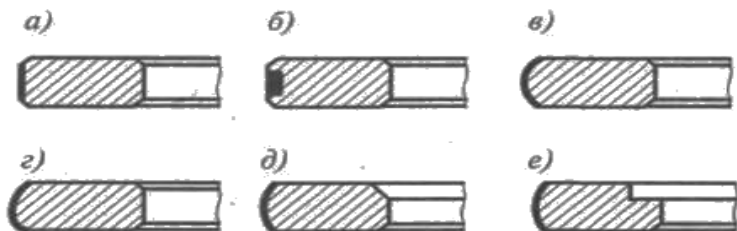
Профили верхних компрессионных колец двигателей легковых автомобилей:
